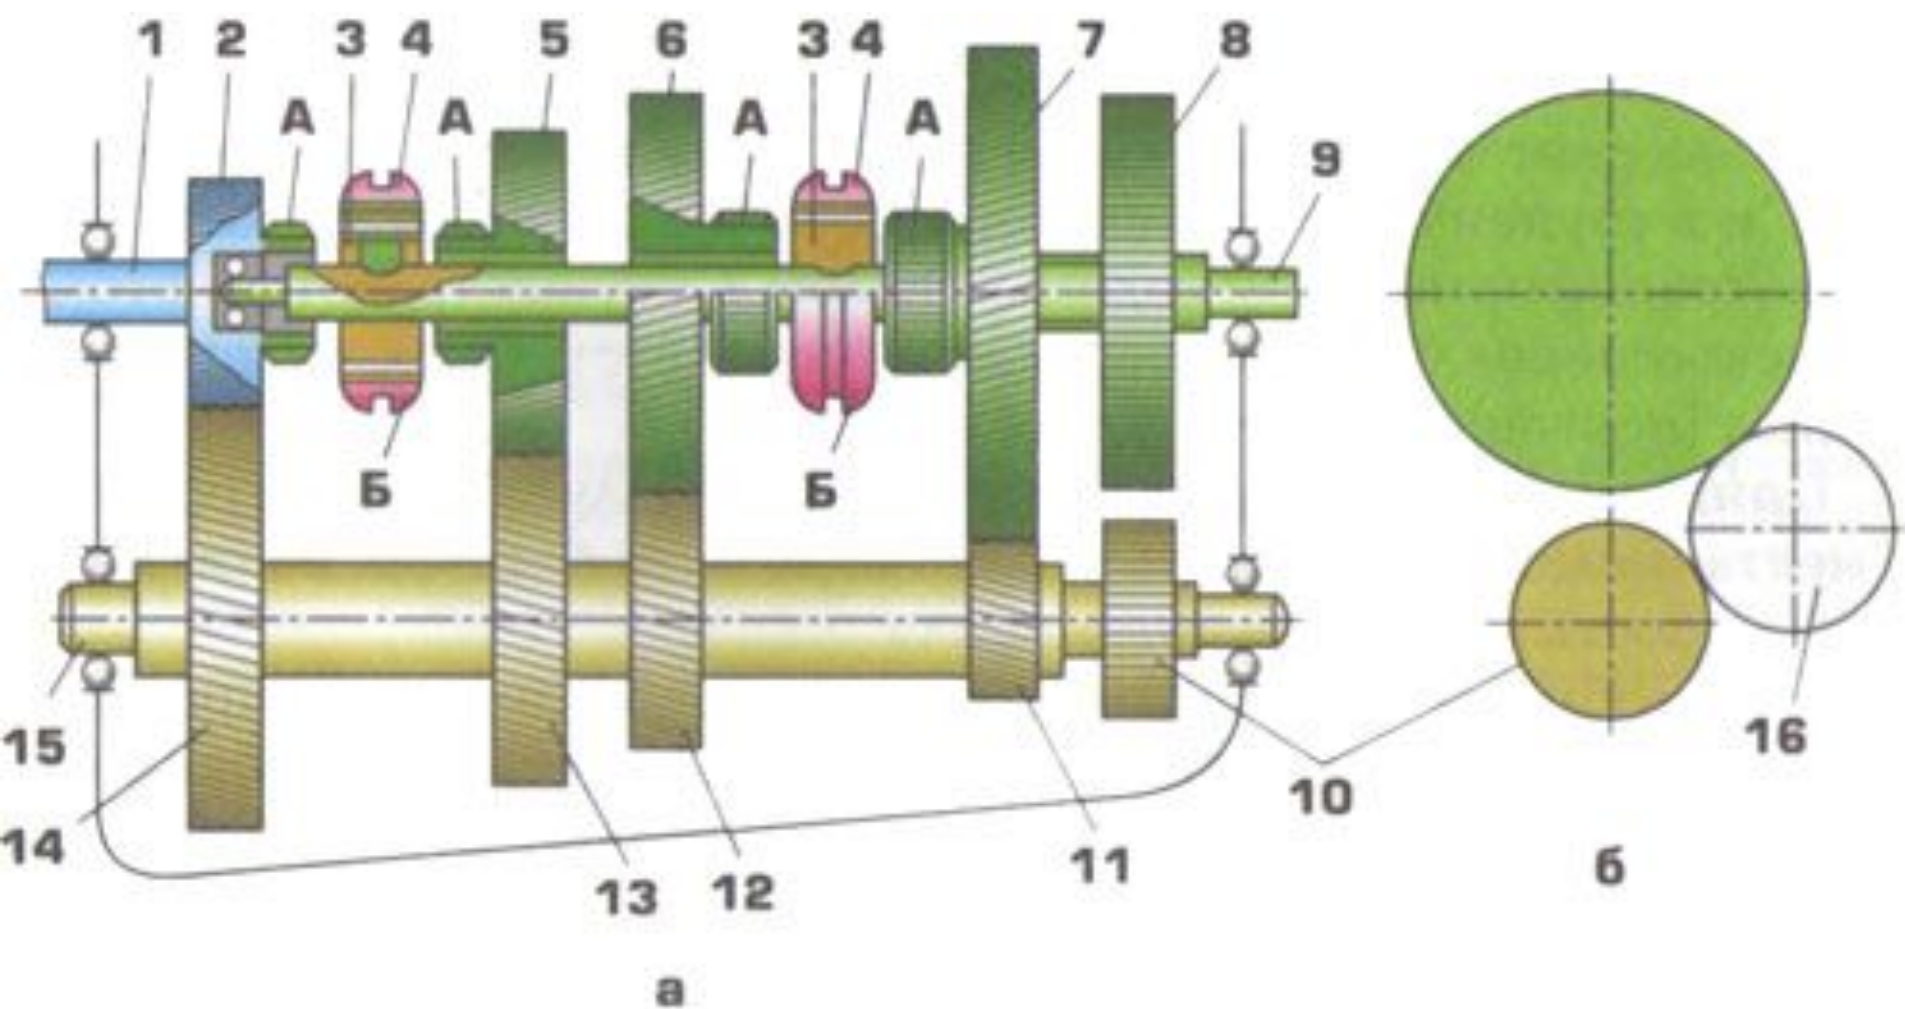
Схема коробки передач с постоянно зацепленными шестернями:
